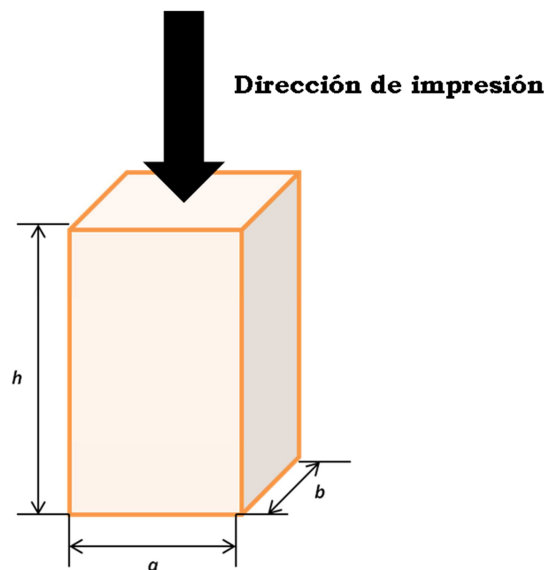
Esquema de una probeta utilizada en un ensayo de compresión.
